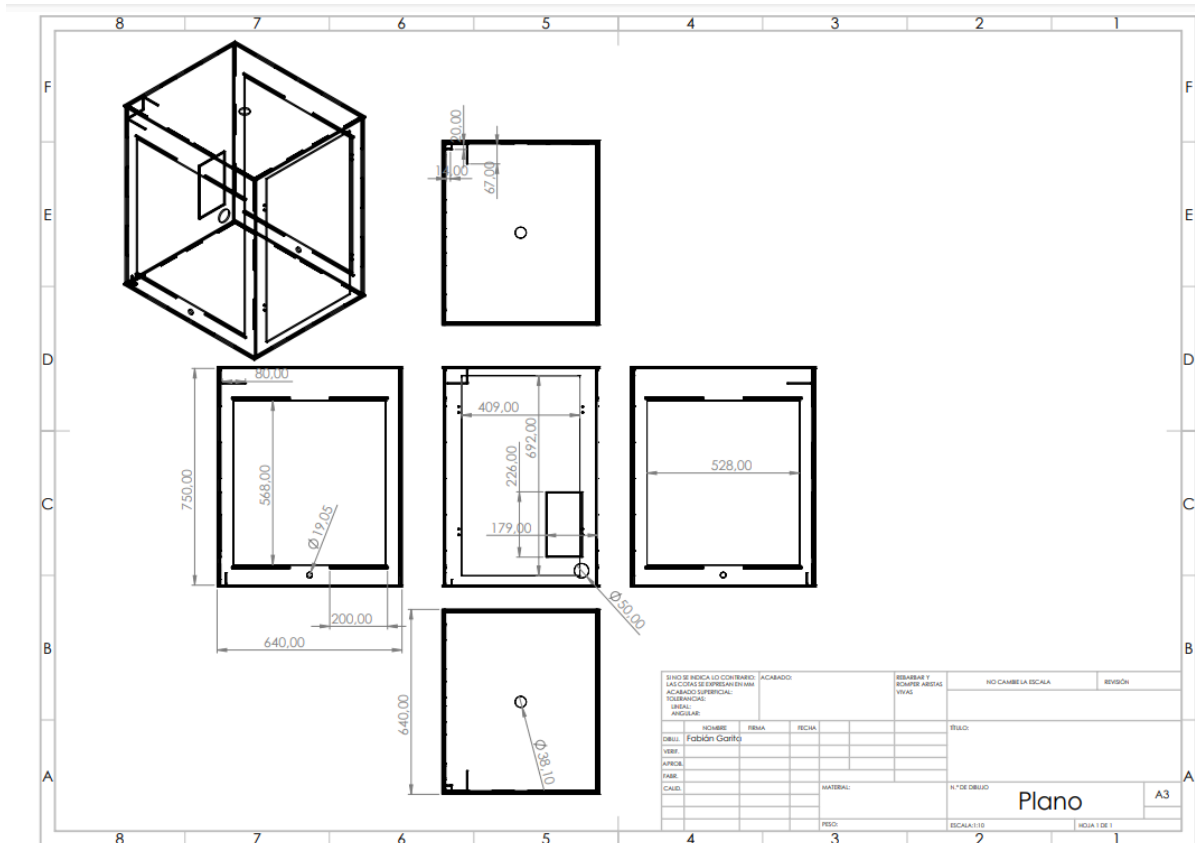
Plano de construcción de la cámara de fabricación propuesta.
